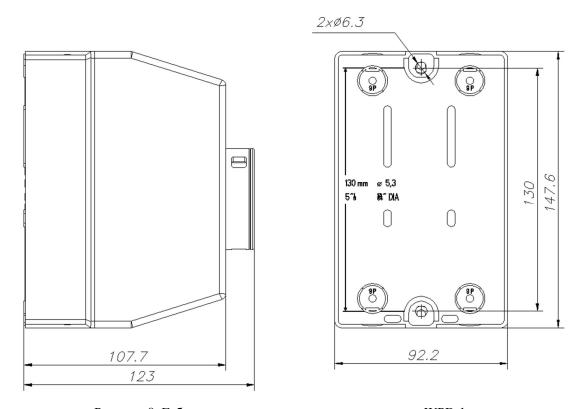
Габаритные и присоединительные размеры WPB-1
